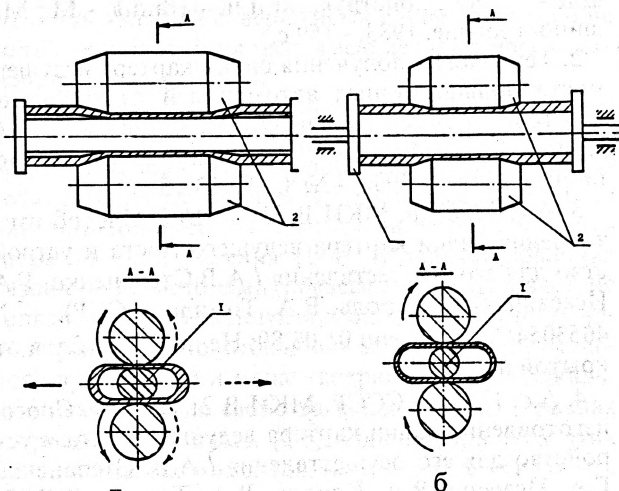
Способ изготовления картера ведущего моста методом: а – продольной прокатки; б – поперечной прокатки
